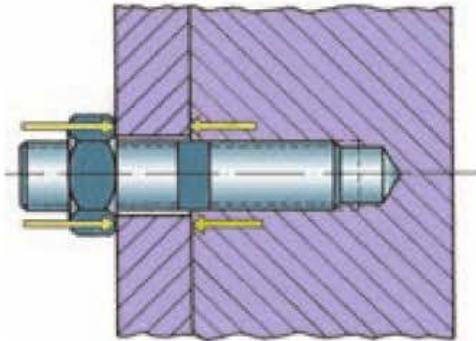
Ensamblaje atornillado mediante tornillo sin cabeza, tuerca y la pieza.
